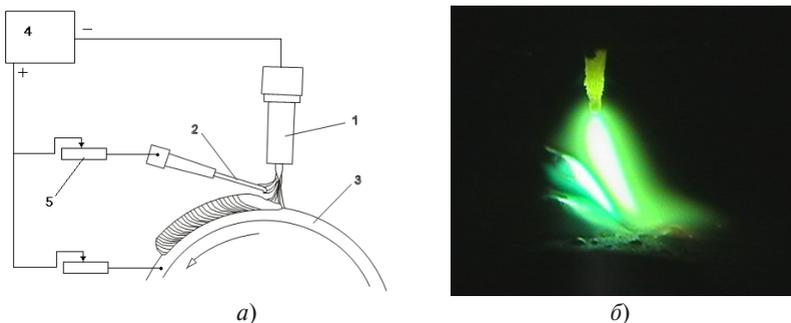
Процесс наплавки: *а)* схема процесса: 1 – горелка, 2 – сварочная проволока, 3 – основной металл, балластное сопротивление; *б)* фотография процесса
